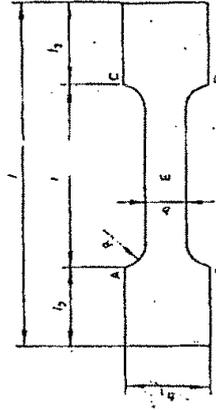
Forma y dimensiones de la pieza de ensayo
